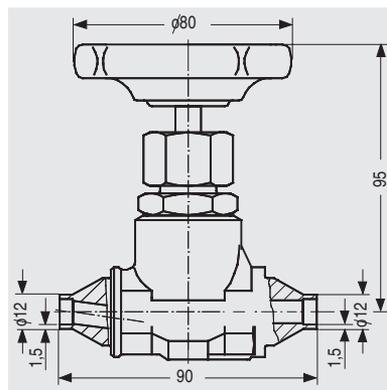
/136 Запорный вентиль 7MF9017-1E, размеры
